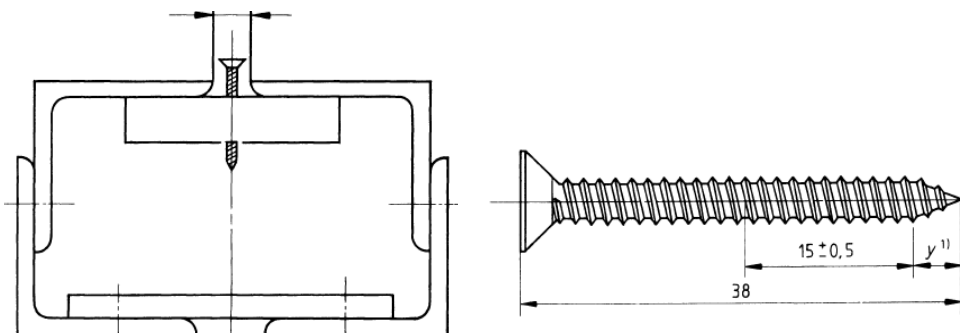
Dispositivo de teste (esquerda) e parafuso de ensaio (direita) [32].
